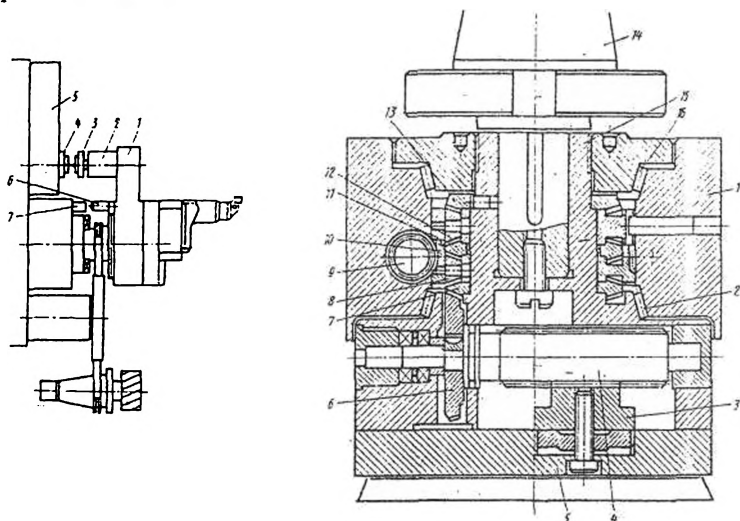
Головка з радіальною подачею інструмента:
